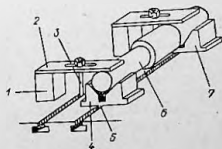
Fixarea unui semifabricat de formă cilindrică pe masa mașinii cu ajutorul reazemelor în V.
